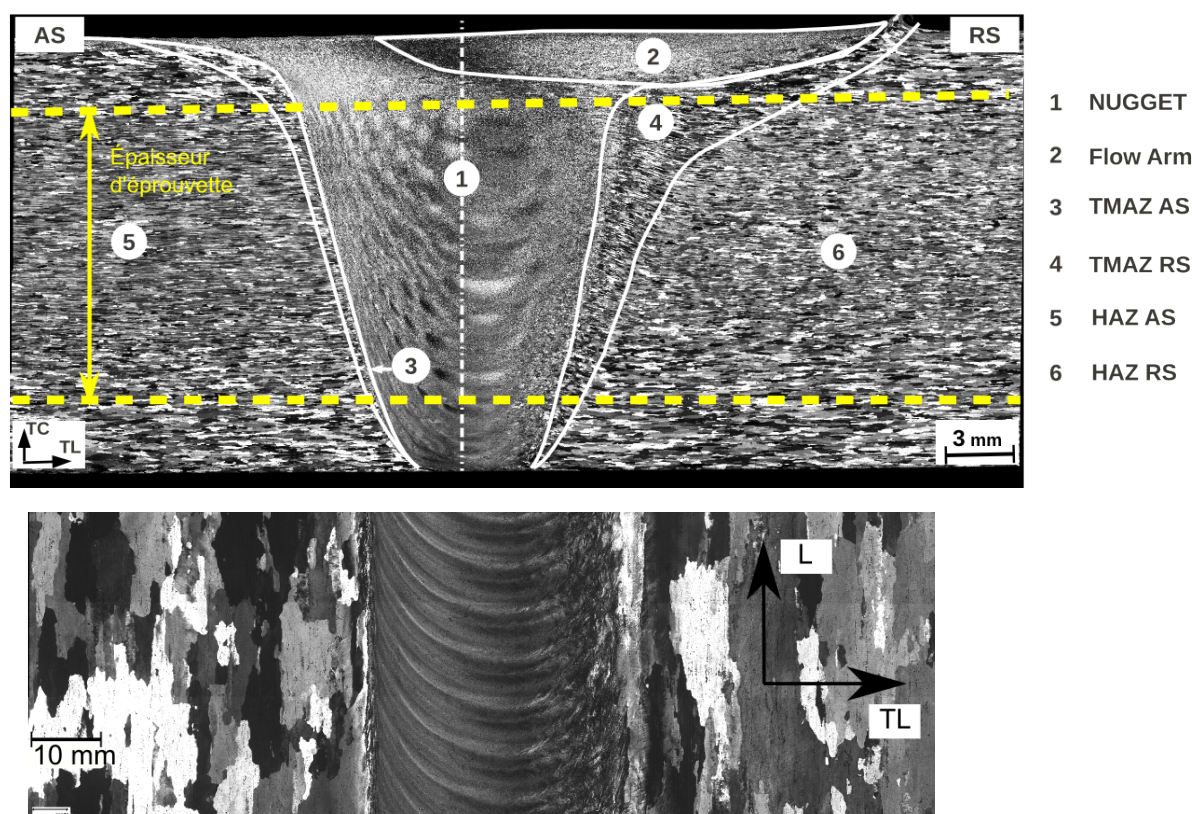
Macrostructure du joint soudé par FSW en alliage d'aluminium 2050-T851
